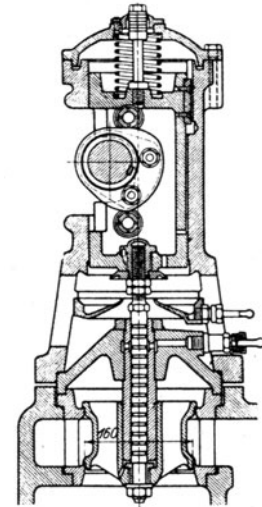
Herzscheibe zur Gruppenventilsteuerung.
